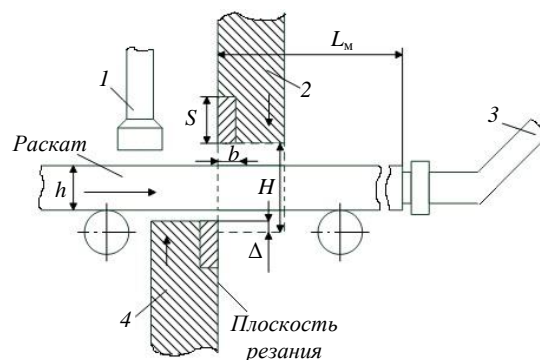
Схема резки раската на ножницах с параллельными ножами: 1 – прижим; 2 – верхний нож; 3 – передвижной упор; 4 – нижний нож
